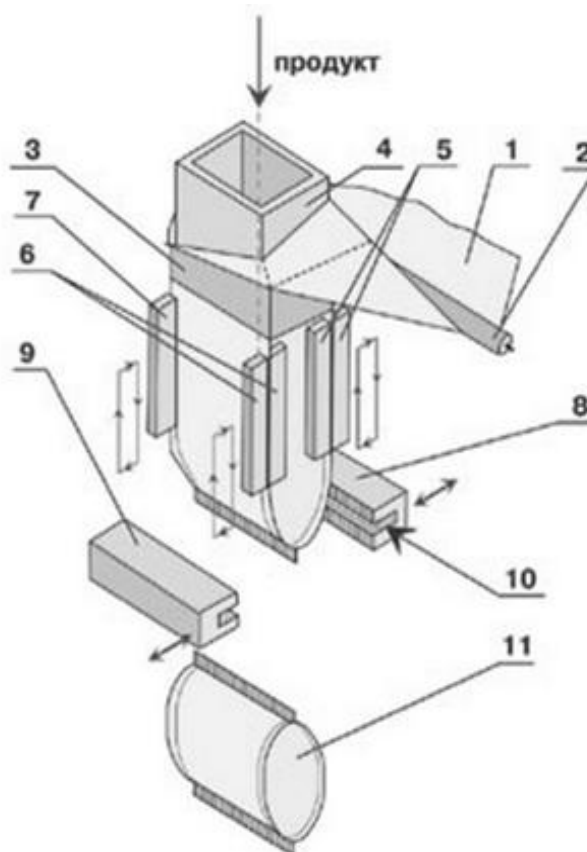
Схема машини із комірцем періодичної дії з протягуючими губками поздовжнього шва зварювання: 1 - пакувальний матеріал; 2 - напрямний ролик; 3 - комірець; 4 - прямокутного перерізу трубопровід; 5, 6, 7 - поздовжні губки зварювання; 8, 9 - поперечно-зварні головки; 10 - ніж; 11 - споживча упаковка.
